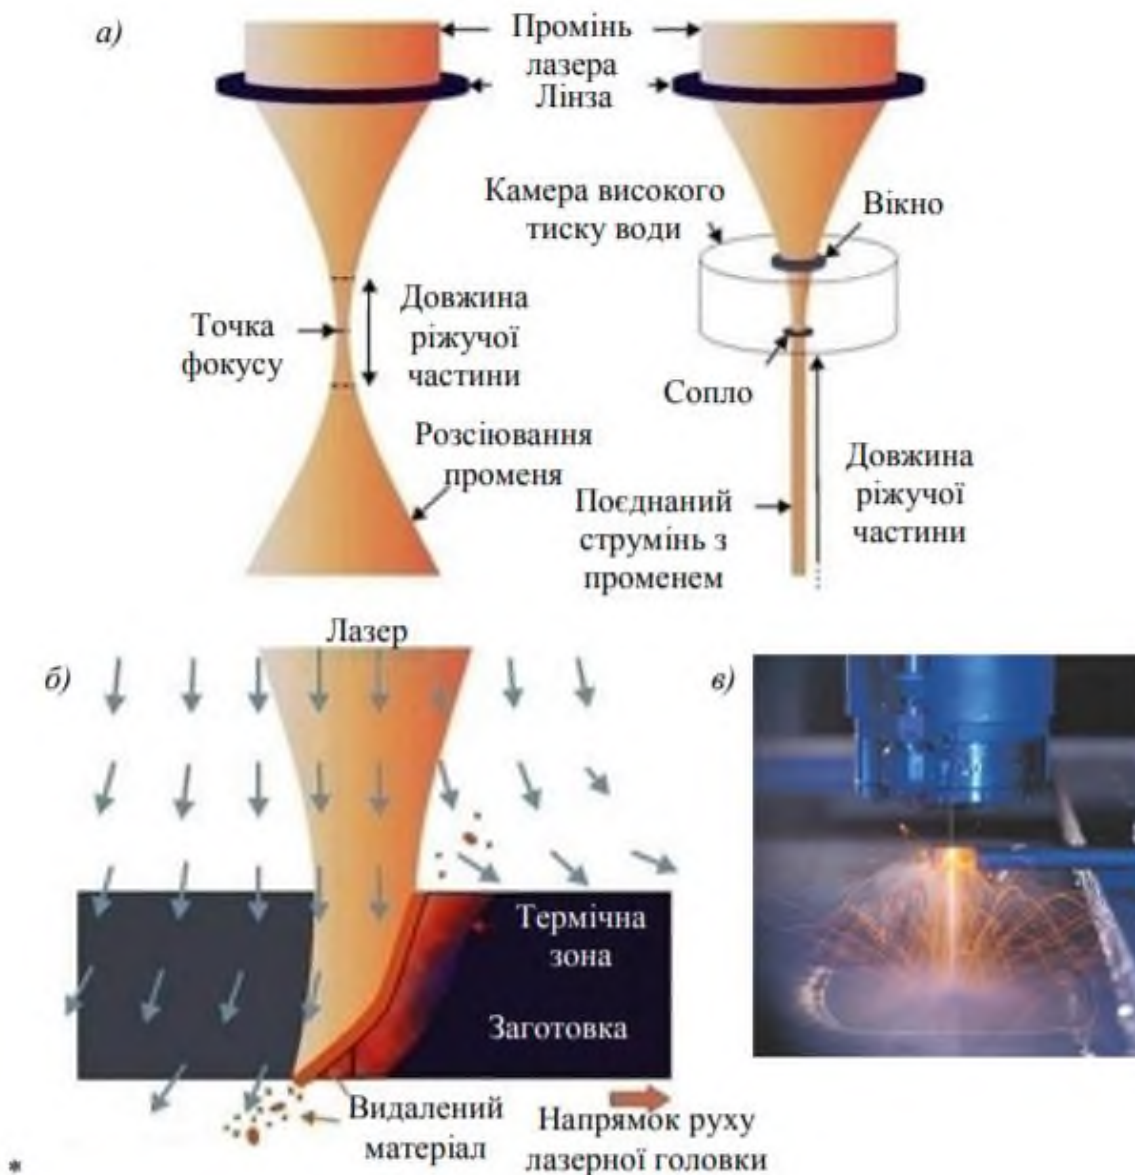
Принцип формування струминно-лазерного потоку та його вплив на оброблювану заготовку [35]: а і б – формування струминно-лазерного потоку; в – різання листової заготовки
